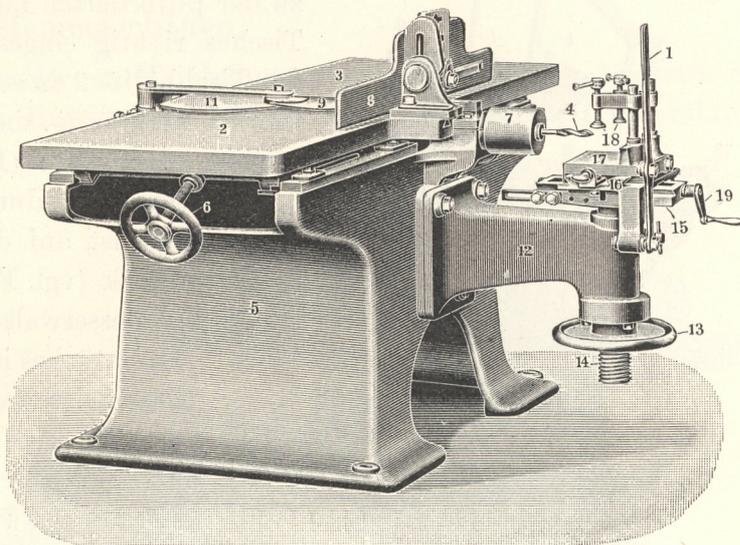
Abrichtmaschine mit Bohrvorrichtung.
